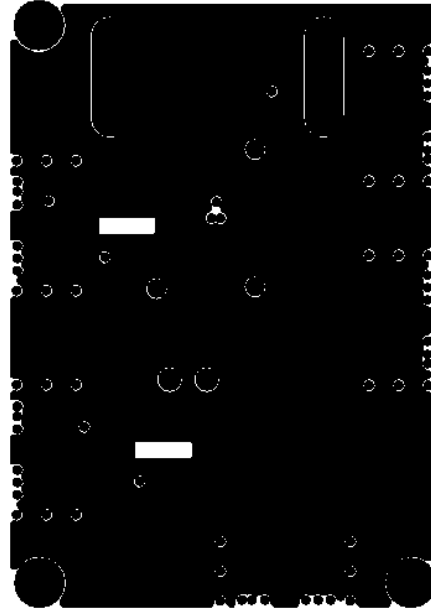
MAX3744/MAX3745 评估板 PCB 布线
